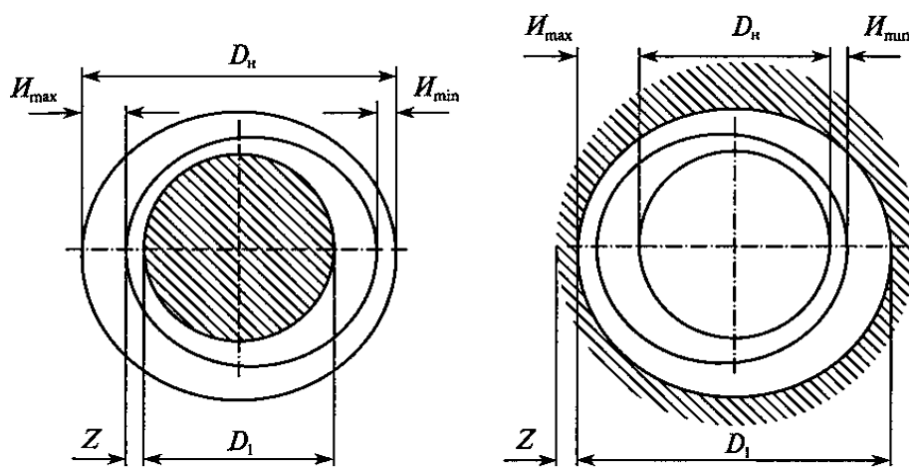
Схеми обробки валу та отвору під ремонтний розмір [13]
